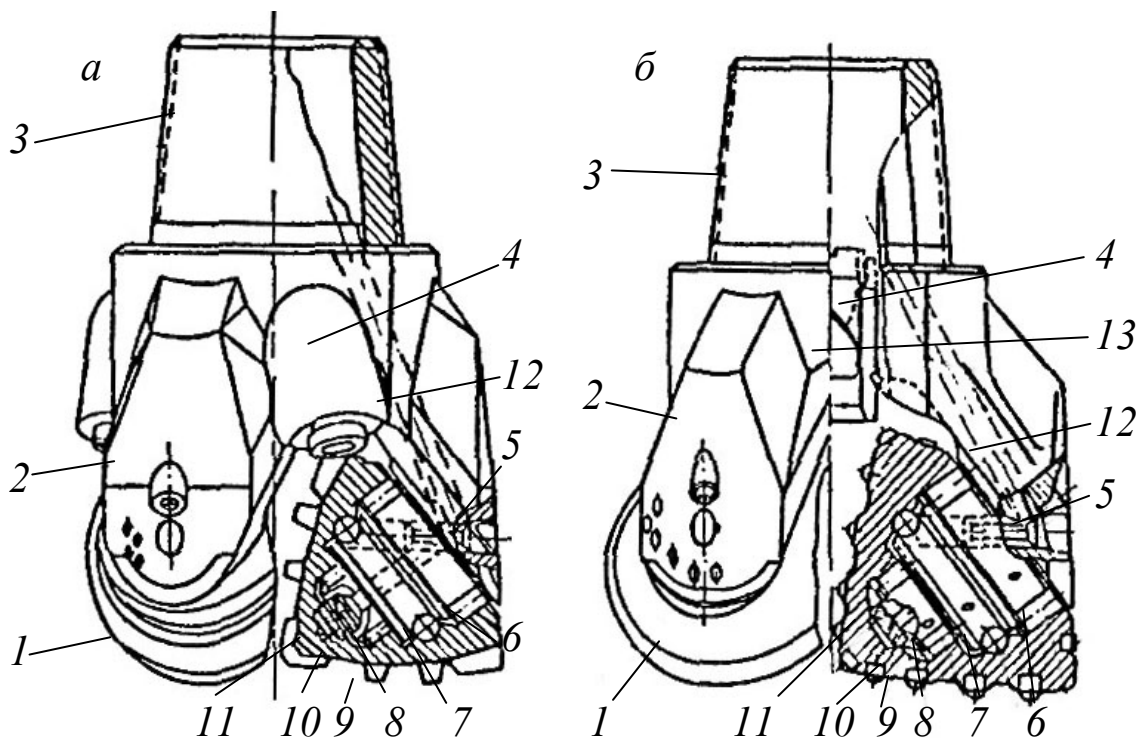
Конструктивные схемы трехшарошечных долот: *а* – зубчатого с фрезерованным вооружением шарошек и периферийной продувкой; *б* – штыревого с вооружением цилиндрическими элементами из твердого сплава и центральной продувкой
